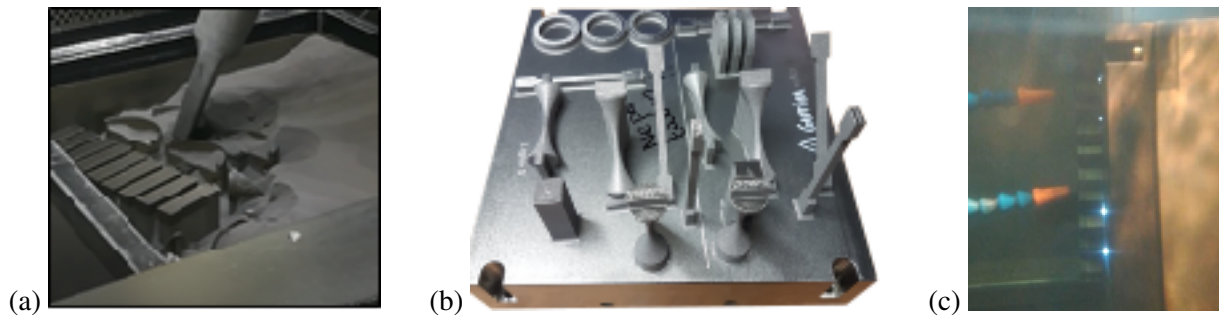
(a) Retrait de la poudre en excès, (b) plateforme de fabrication extraite de la machine avec les pièces fabriquées et (c) découpe fil par électro-érosion pour désolidariser les pièces de la plateforme de fabrication.
